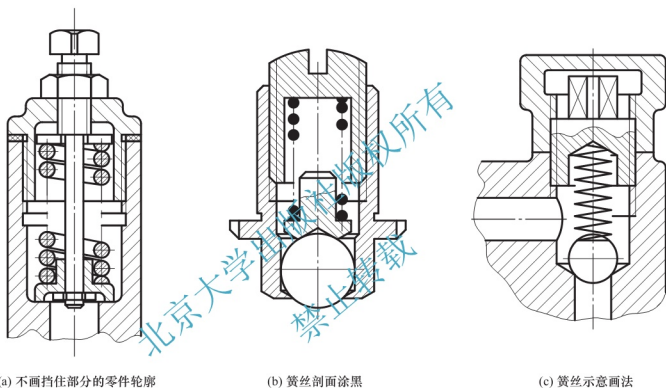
圆柱螺旋压缩弹簧在装配图中的画法
